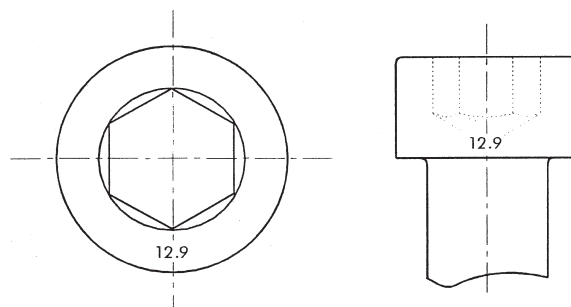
Abb. H: Beispiel für die Kennzeichnung von Zylinderschrauben mit Innensechskant
